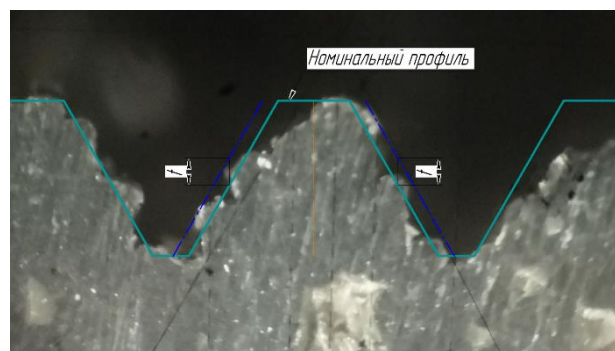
Профиль резьбы M8, сформированной в образце из ABS-пластика
